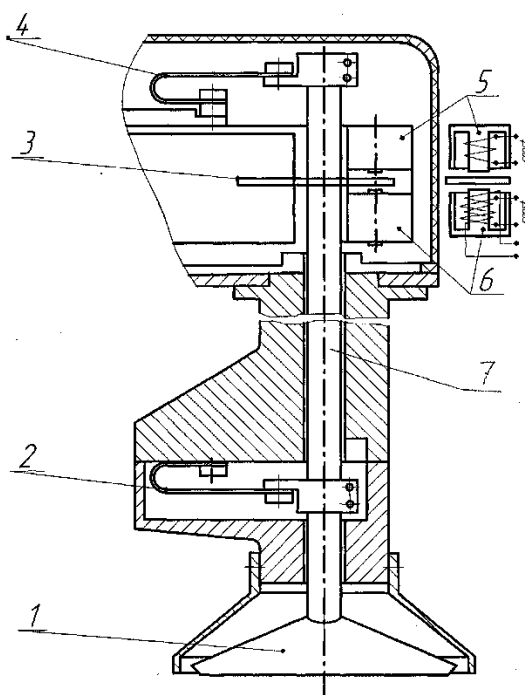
Устройство для непрерывного контроля обрабатываемой прерывистой поверхности
